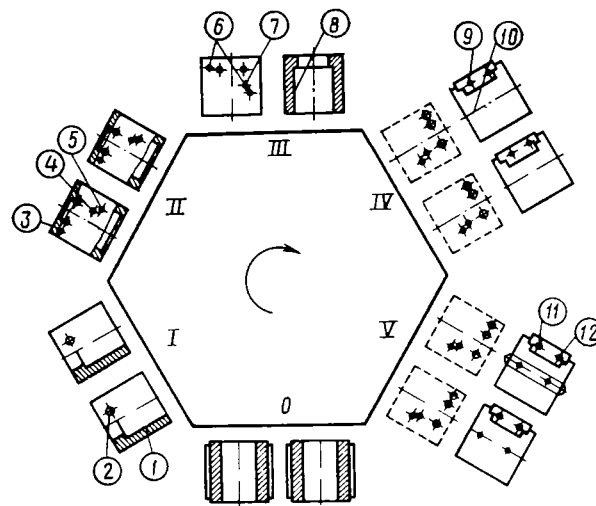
Шестипозиционный агрегатный станок с автоматической установкой и снятием корпусов при механической обработке:
